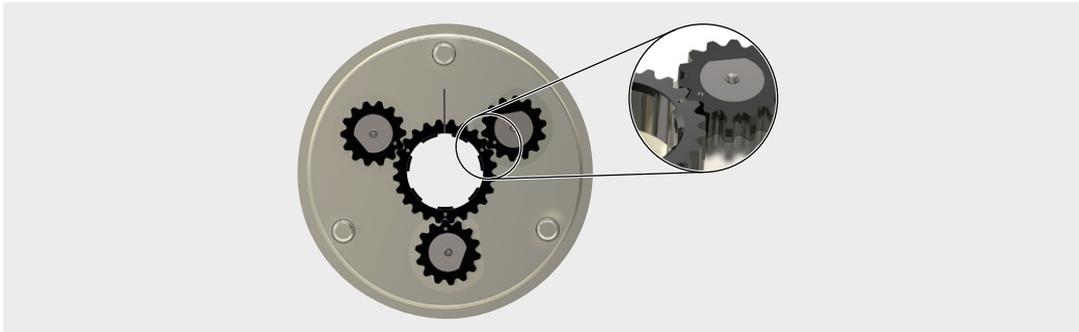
Ausgerichtete Zahnräder des Rollenkäfigs
